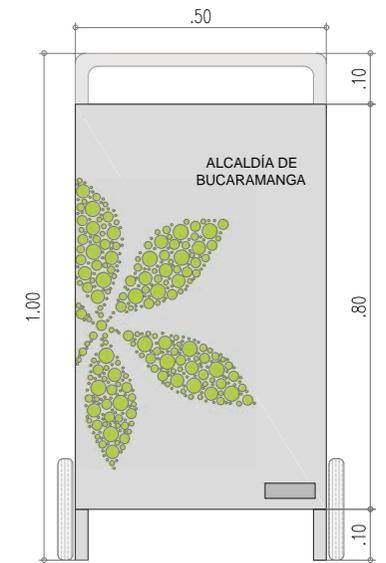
Fachada puesto de venta ambulante tipo 3. Esc 1:15
